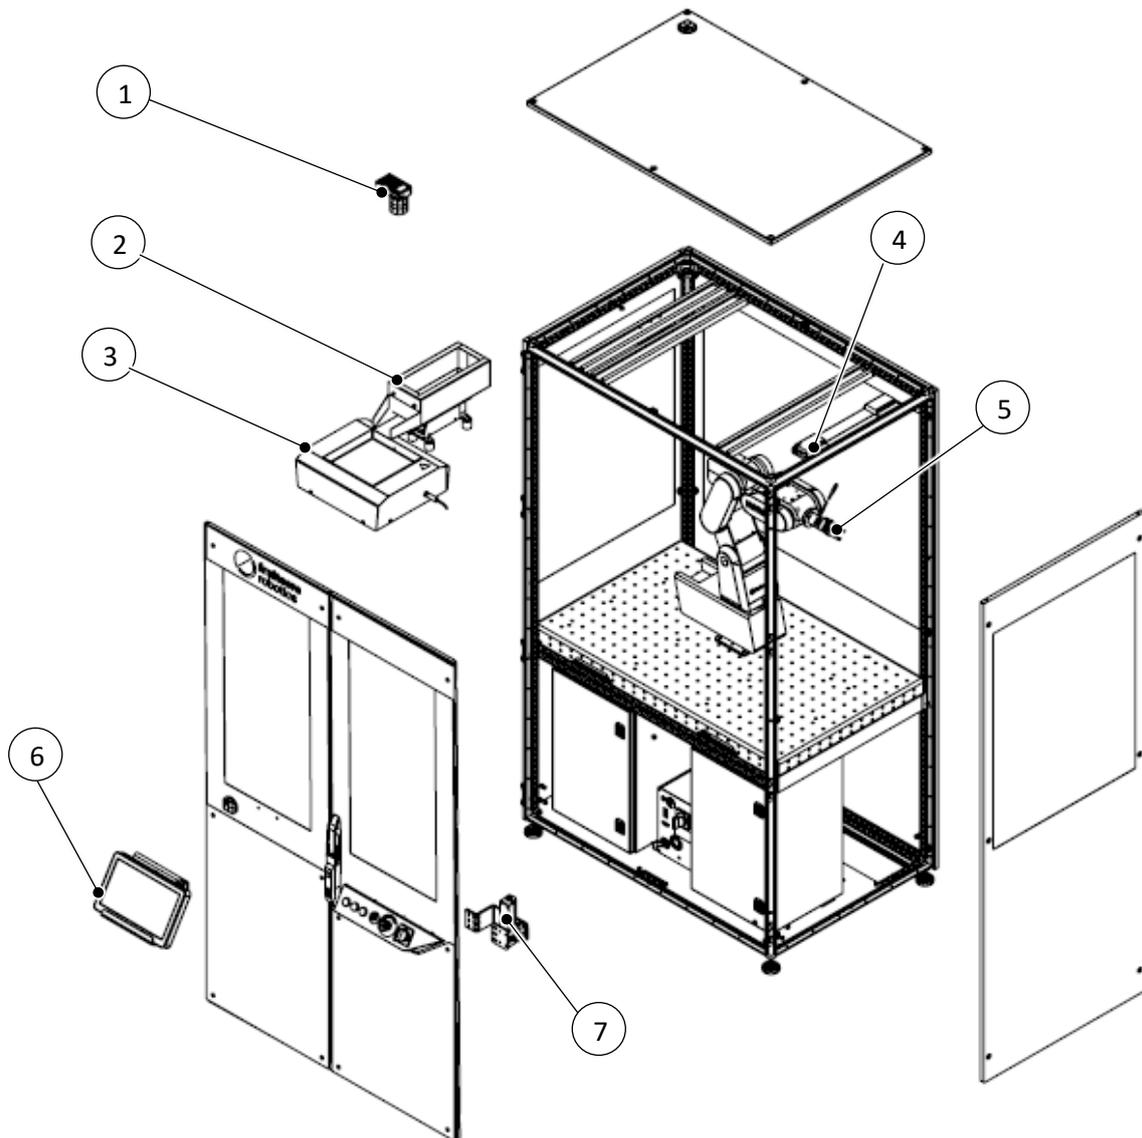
Solution Kit Part Separation - Explosionsansicht
